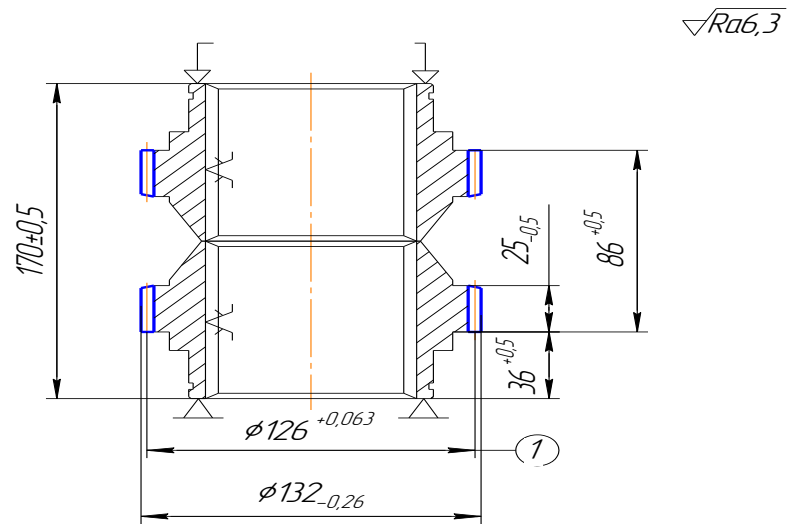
Ескіз на зубофрезерну операцію
